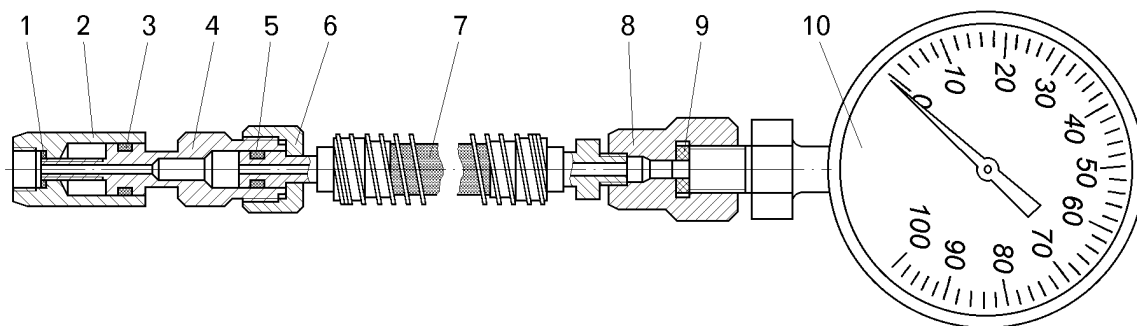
Приспособление для замера давления в цилиндрах подвески:
